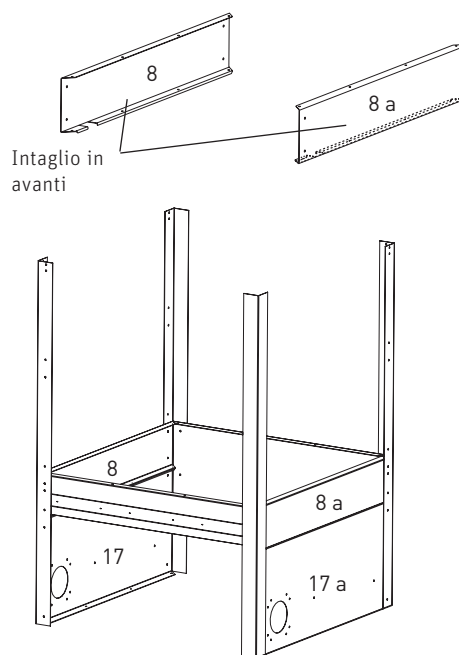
Montaggio delle pareti laterali dell'unità di commutazione e degli elementi di collegamento orizzontali
